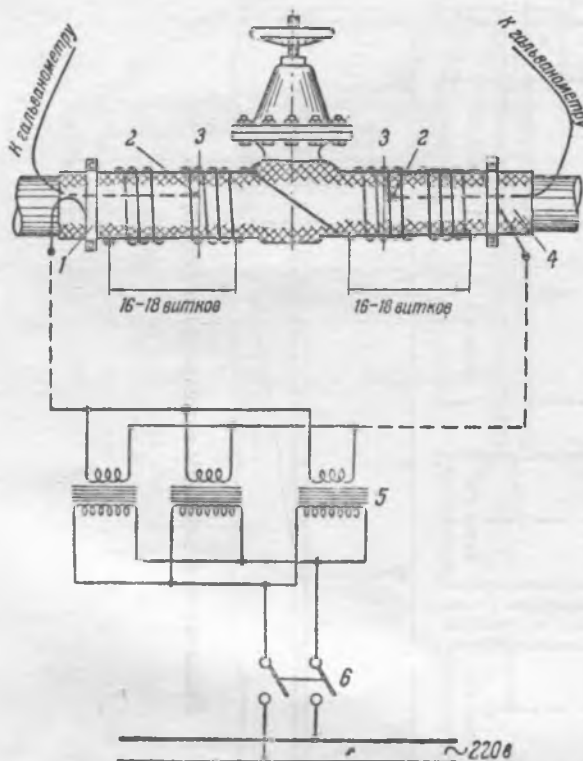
Схема термообработки сварных стыков трубопроводов.
